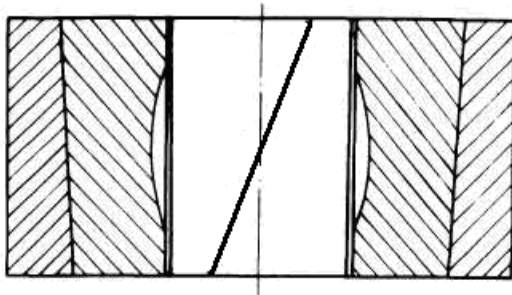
Схема штамповки деталей с наклонным сварным швом
